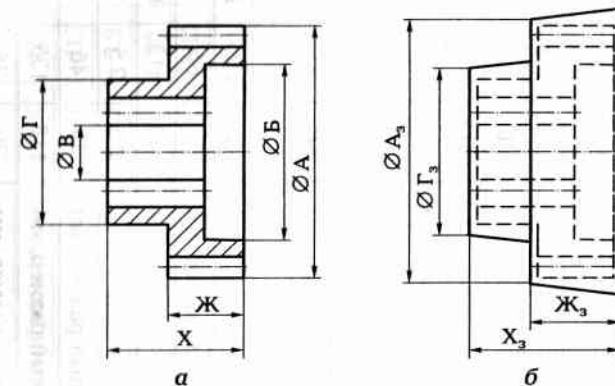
Эскиз обрабатываемого цилиндрического зубчатого колеса с внутренними прямоугольными шлицами:
